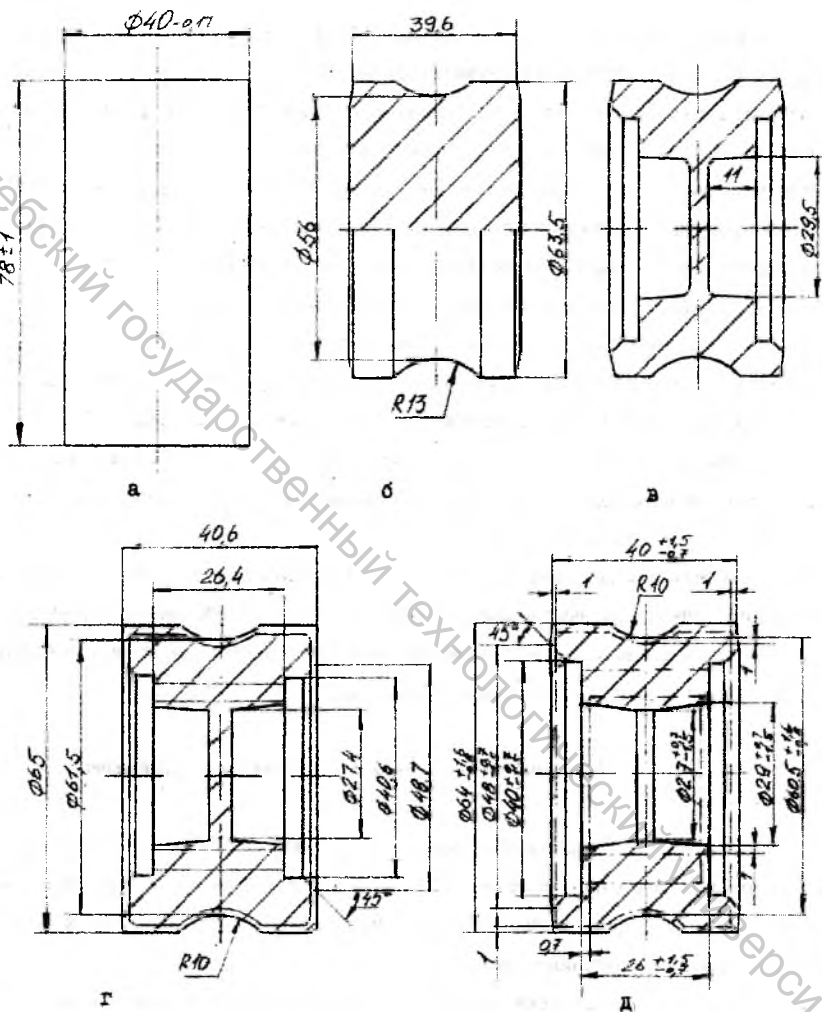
Переходы штамповки и чертеж поковки шестерни
